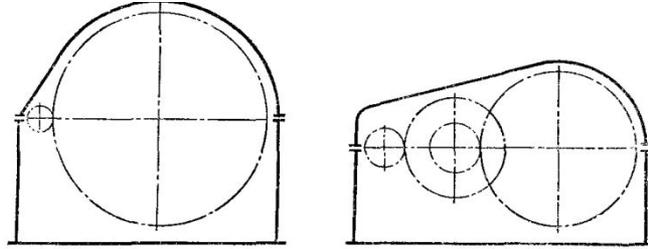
Сопоставление габаритов одноступенчатого и двухступенчатого редукторов с цилиндрическими колесами при одинаковом передаточном числе $i = 8,5$
